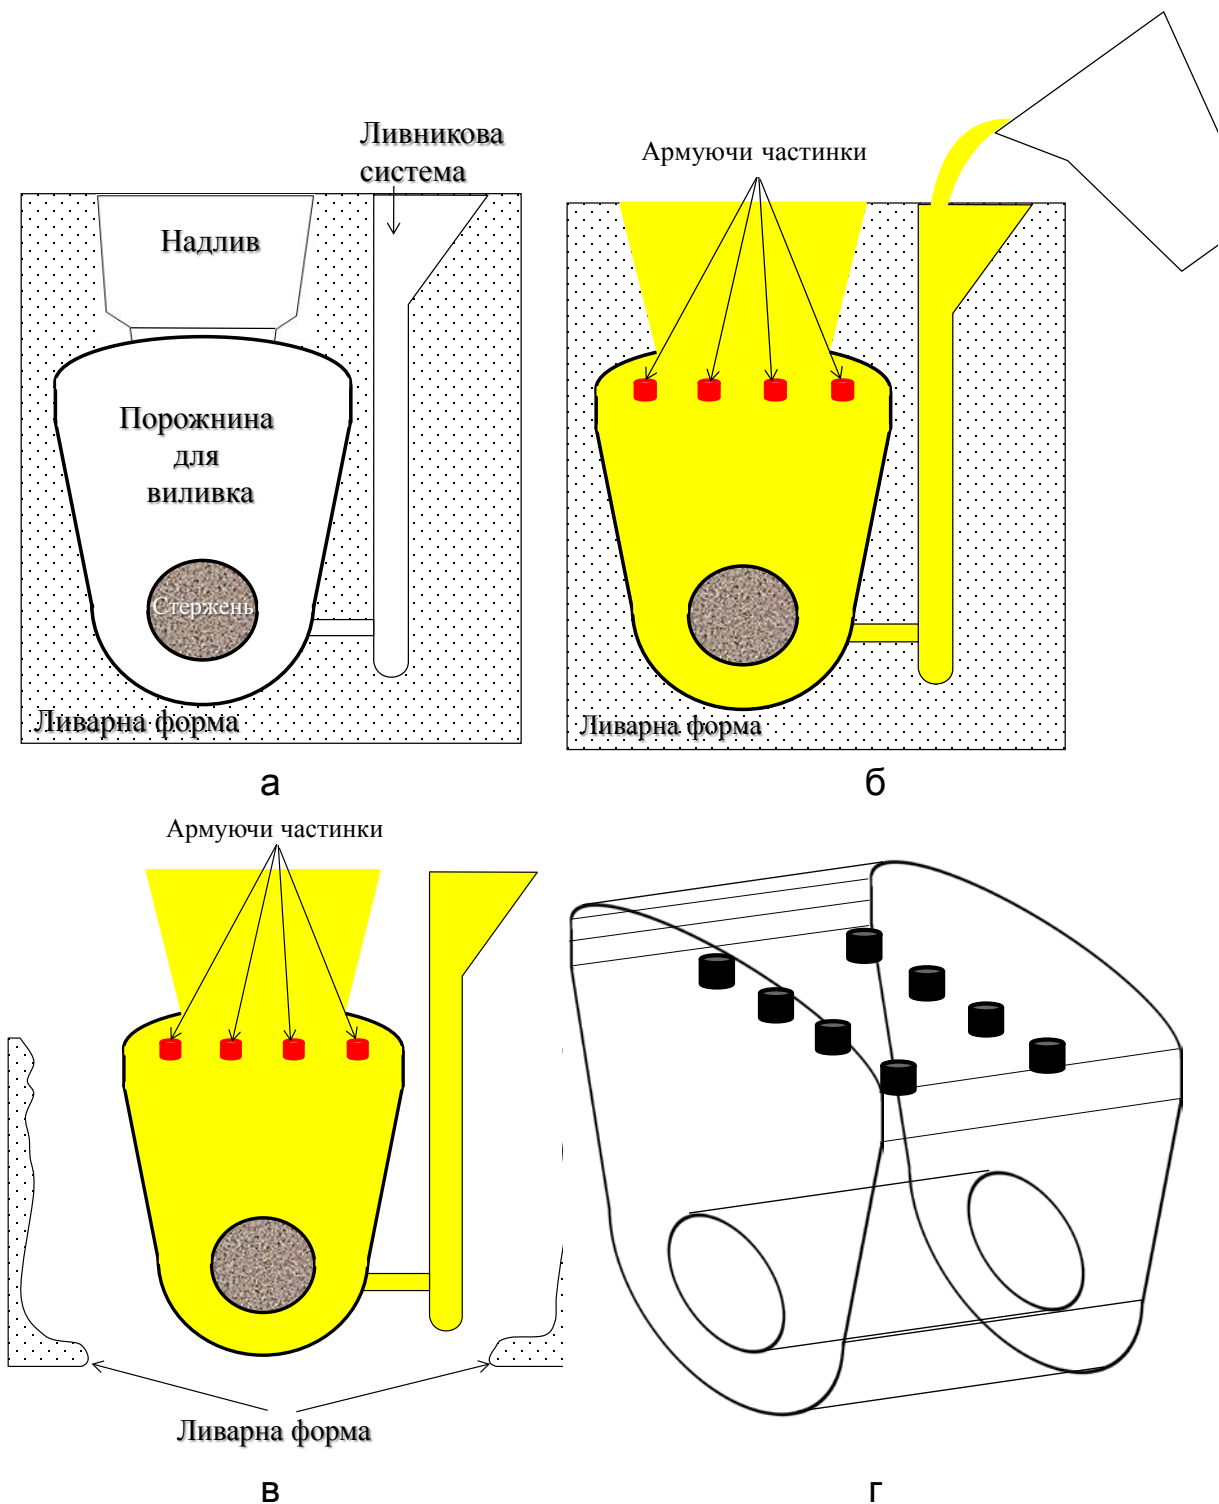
Технологія виготовлення дисперсезміцнених композиційних виробів шляхом лиття: а – зібрана ливарна форма; б – заливання матричним розплавом ливарної форми з армуючими частинками; в – витяг композиційних виливків з ливарної форми після затвердіння та охолодження; г – композиційна виливка після очистки, обрубки та відрізки ливникової системи.
